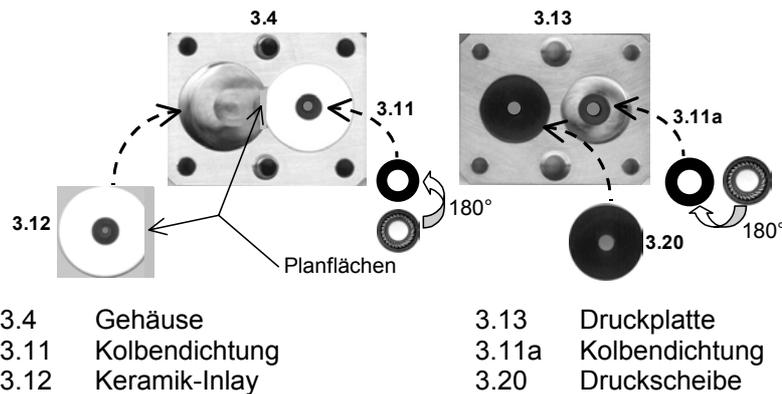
Einzelteile im geöffneten Pumpenkopf
